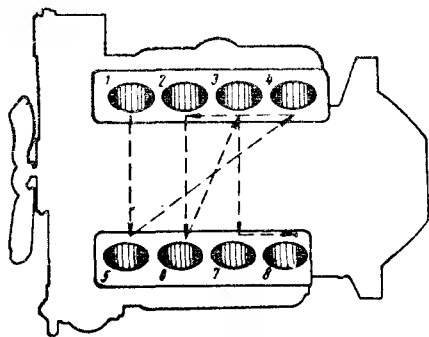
Порядок регулировки клапанов в нескольких цилиндрах при одном и том же положении коленчатого вала
